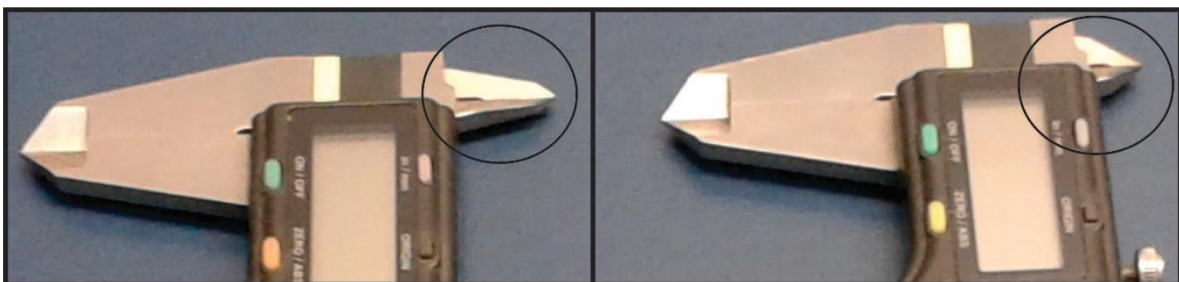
Defecto de fabricación en las puntas de interiores.
